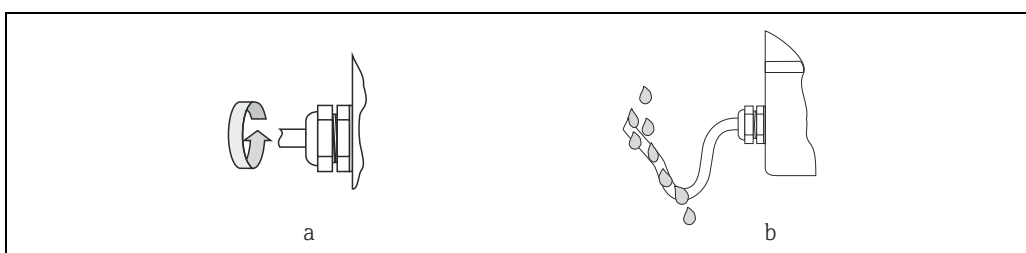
Instrucciones para la instalación, prensaestopas de entrada de cables
